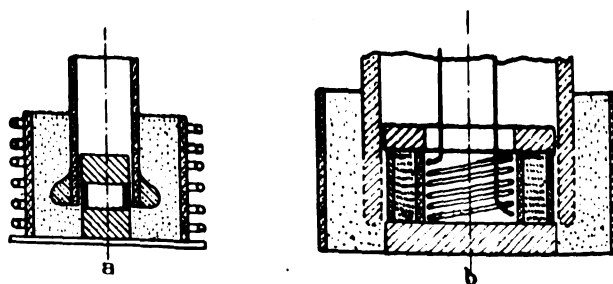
Autres schémas de constitution ou modification de pièces de silice par le chauffage par induction à haute fréquence : a, soudure d'une collerette à un tube; b, fabrication continue de pièces cylindriques.
